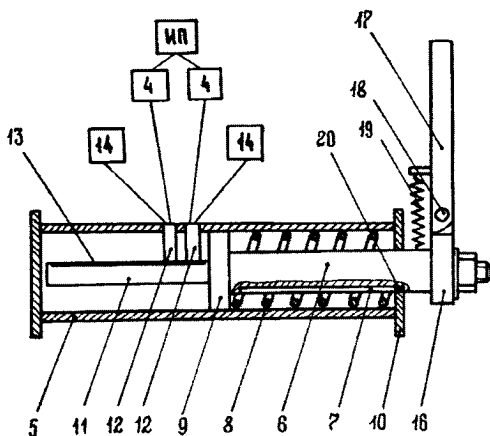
Пристрій для вимірювання довжини контакту шин з опорними поверхнями
